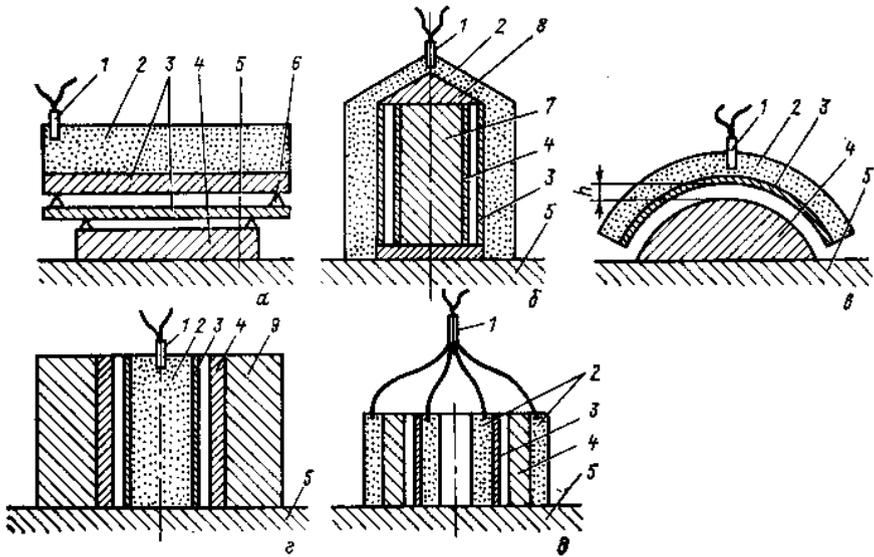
Технологические схемы и оборудование для сварки взрывом:
